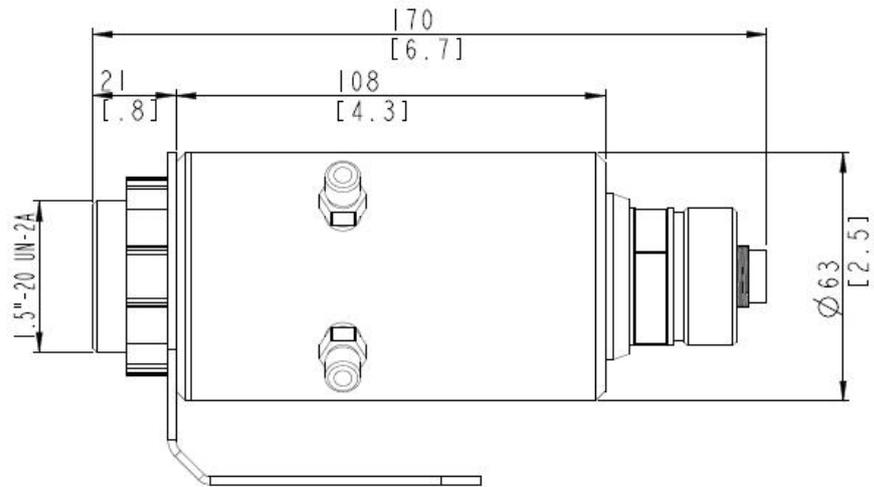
Abmessungen des Sensors mit DIN Stecker und Wasserkühlgehäuse
